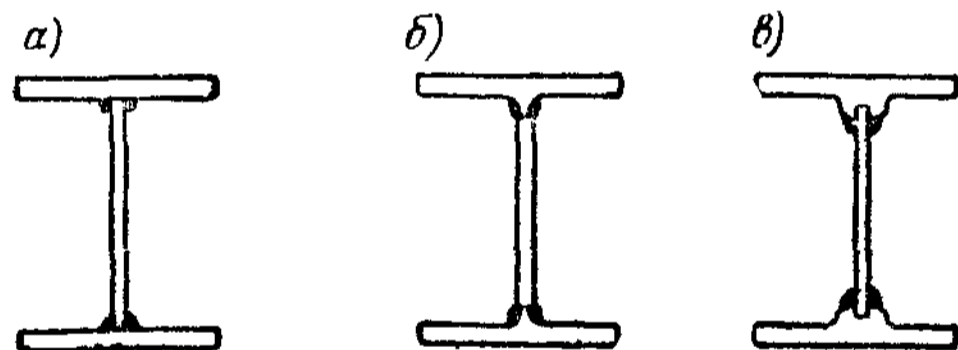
Сварные широкополочные двутавры
